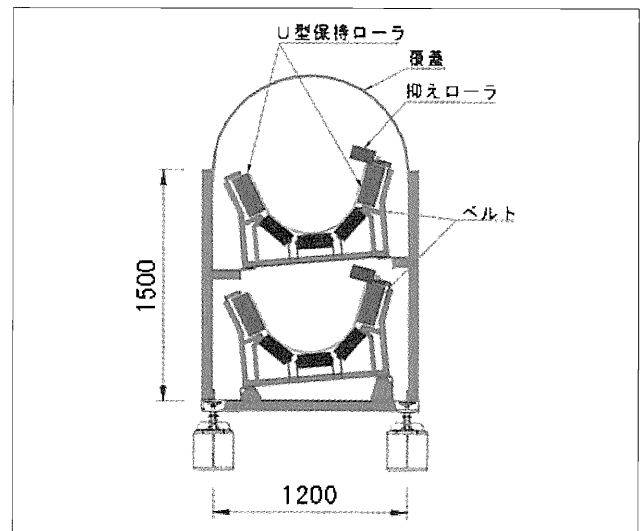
長大カーブベルトコンベヤ (ヘビコン) 断面図
